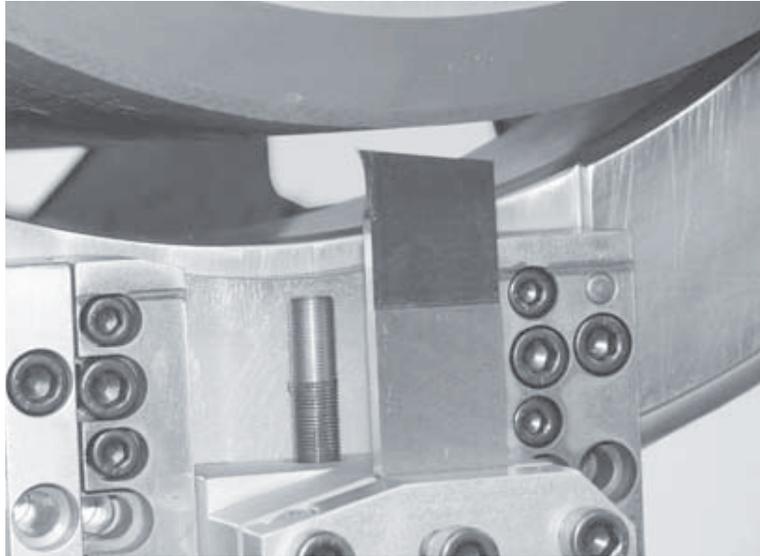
Impostare la punta dell'utensile da taglio a circa 1/8" (3 mm) dalla superficie del tubo.
